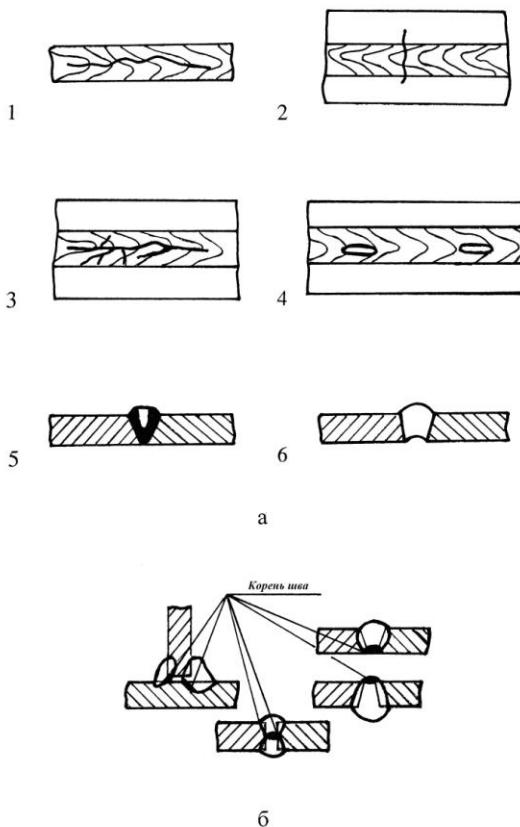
Дефекты сварных соединений (а) и корень шва (б):
